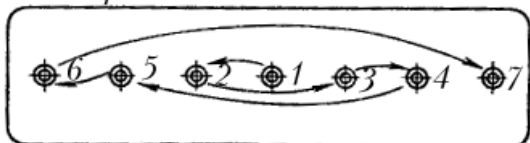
Схема затяжки групповых резьбовых соединений.
